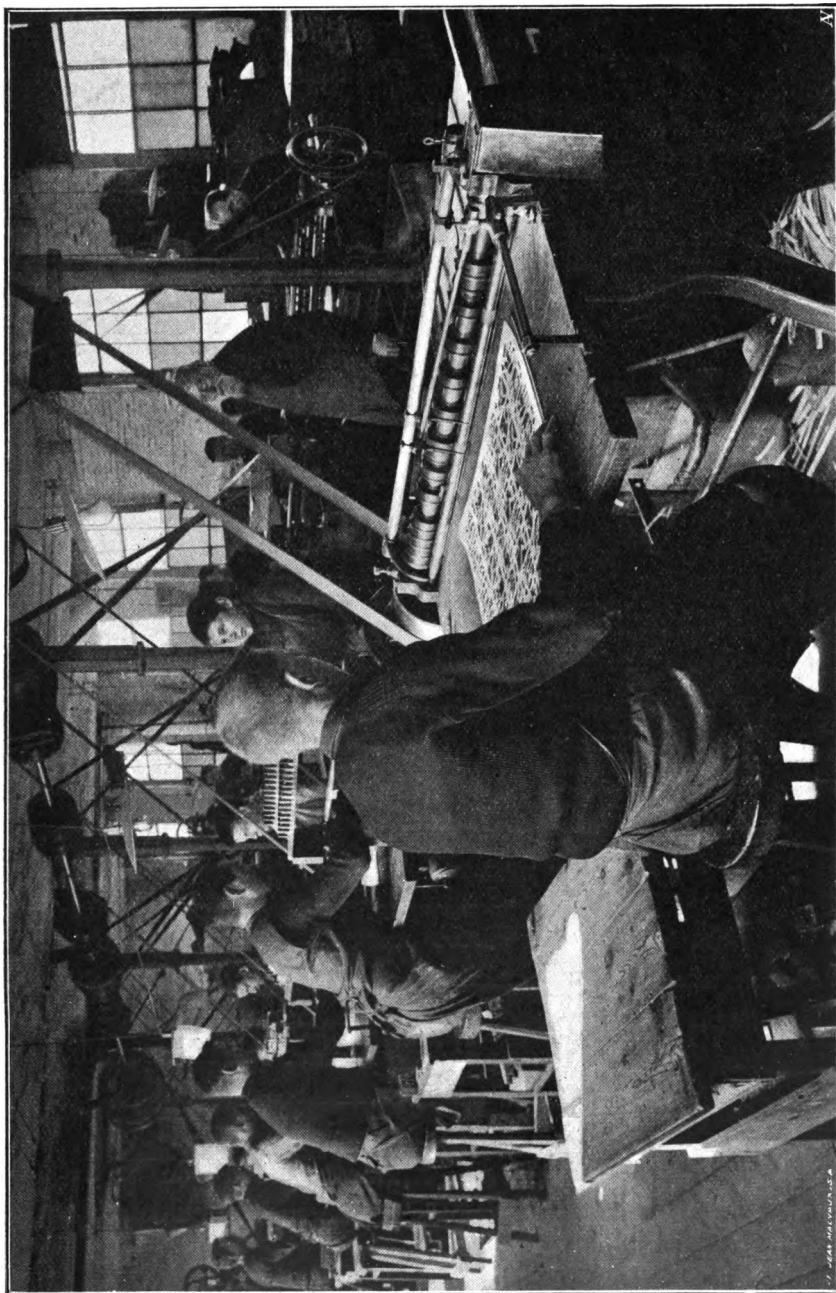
Turnhout : Salle des machines à couper les cartes à jouer.
